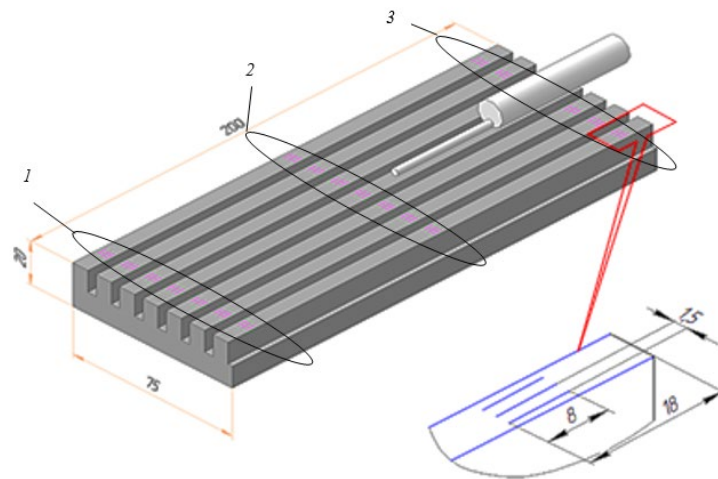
Заготовка и схема измерения шероховатости обработанной поверхности
